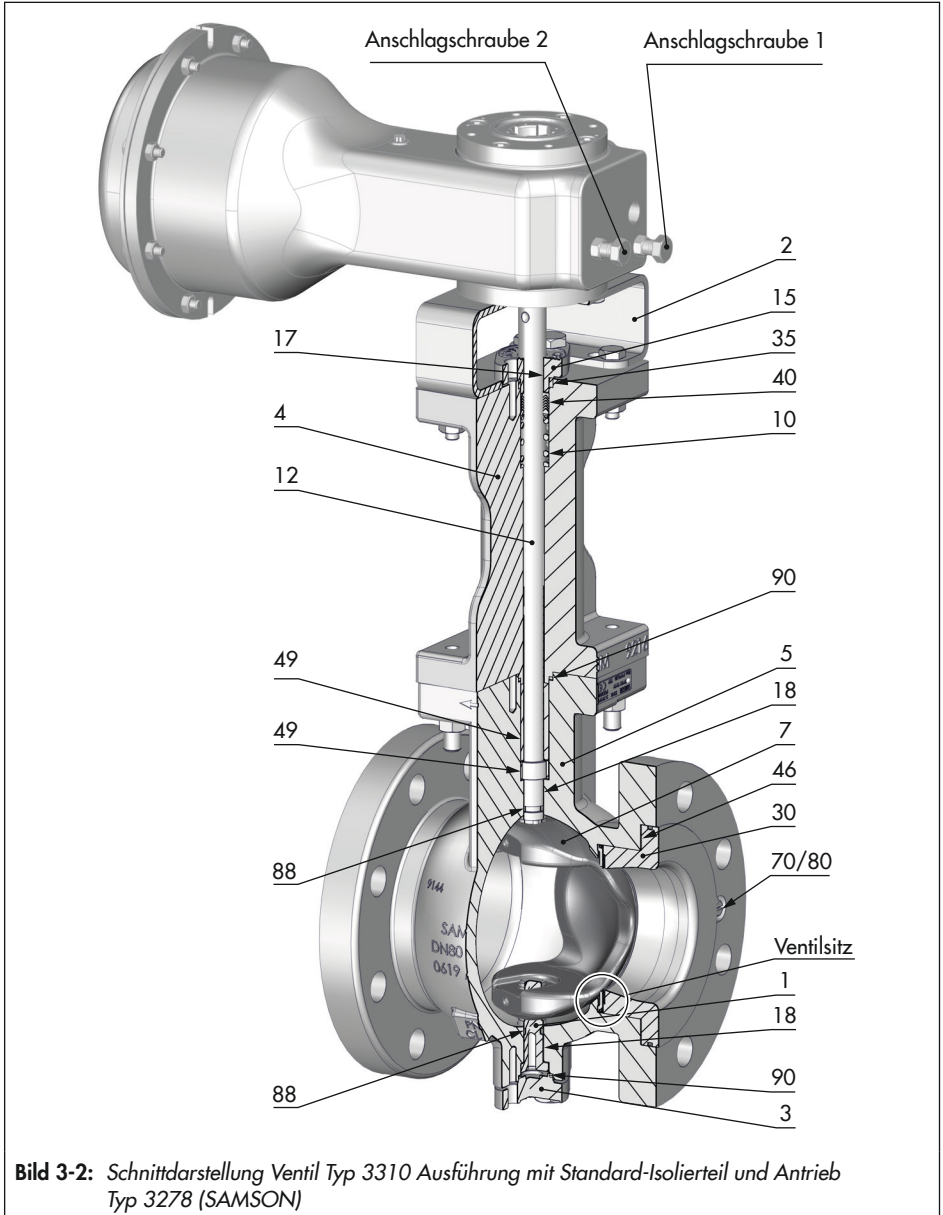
Schnittdarstellung Ventil Typ 3310 Ausführung mit Standard-Isolierteil und Antrieb Typ 3278 (SAMSON)
